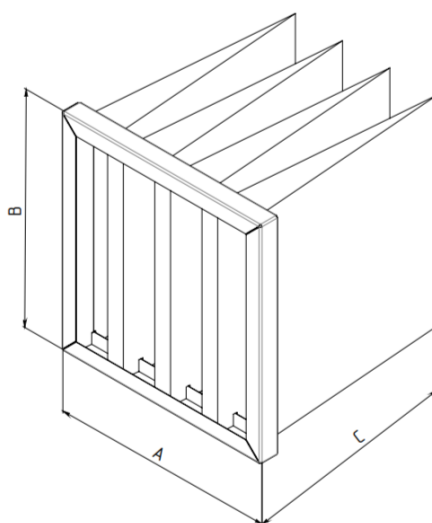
Внешний вид и основные размеры фильтрующих вставок SKR
